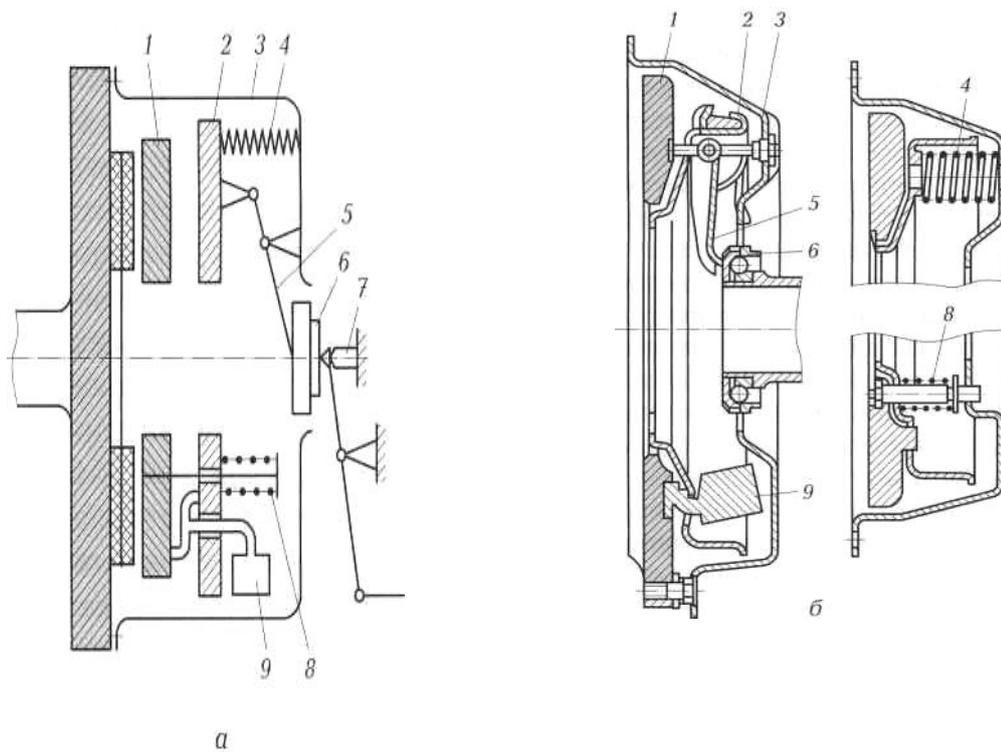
а — схема; б — устройство; 1 — нажимной диск; 2 — реактивный диск; 3 — картер; 4 — пружина; 5 — рычаг выключения сцепления; 6 — подшипник; 7 — упор; 8 — отжимная пружина; 9 — центробежный грузик
